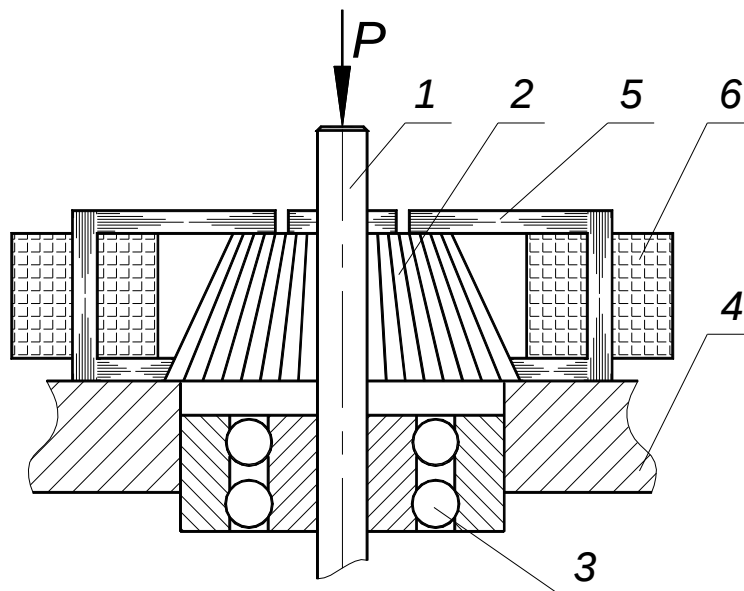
Установка ТПЧ для разборки узла вал-шестерня-подшипник
